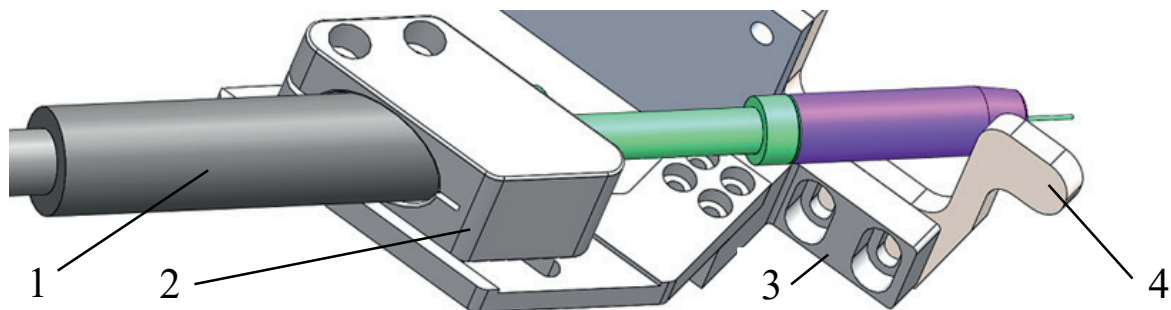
Механизм фиксации и регулировки сварочной горелки: 1 – сварочная горелка, 2 – зажимной блок сварочной горелки, 3 – опорный блок сварочной горелки, 4 – зацеп поперечной арматуры
